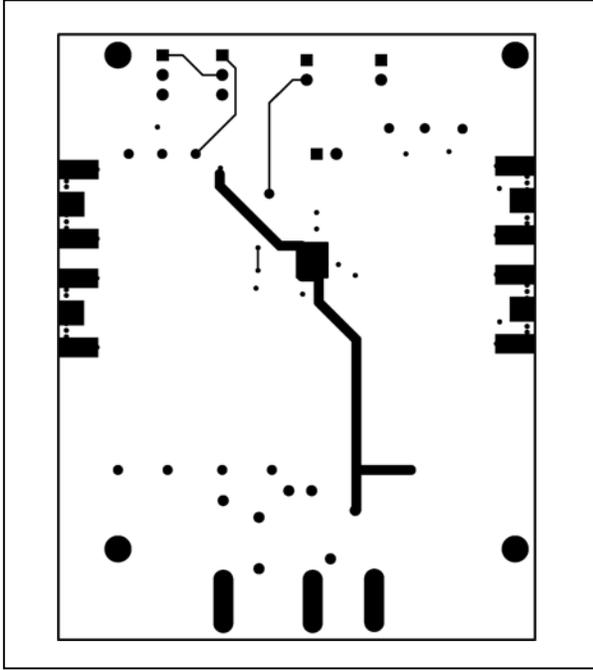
MAX3969 评估板 PCB 布局—焊接层
